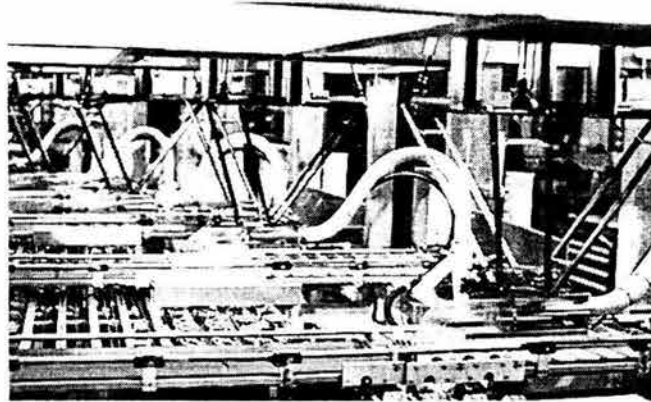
Robot Delta utilizado en el llenado de moldes en una fabrica de galletas.
